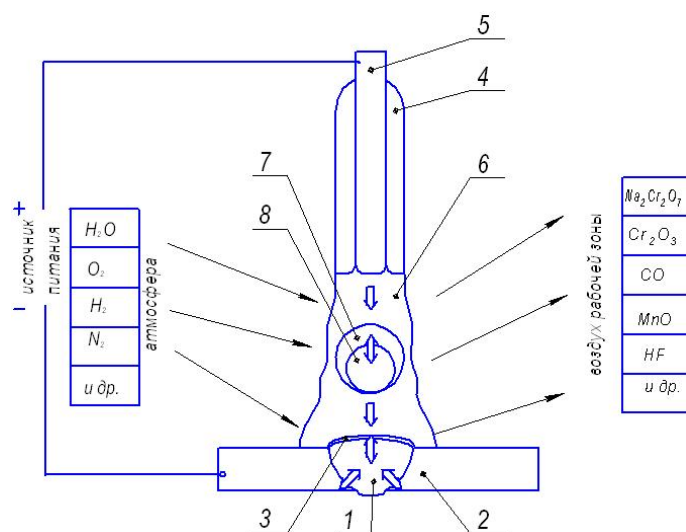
Модель плавления электрода и формирования металла шва: 1 – наплавленный металл; 2 – основной металл; 3 – шлак; 4 – покрытие электрода; 5 – металлический стержень электрода; 6 – газовая атмосфера; 7 – расплавленный шлак капли; 8 – расплавленный металл капли
